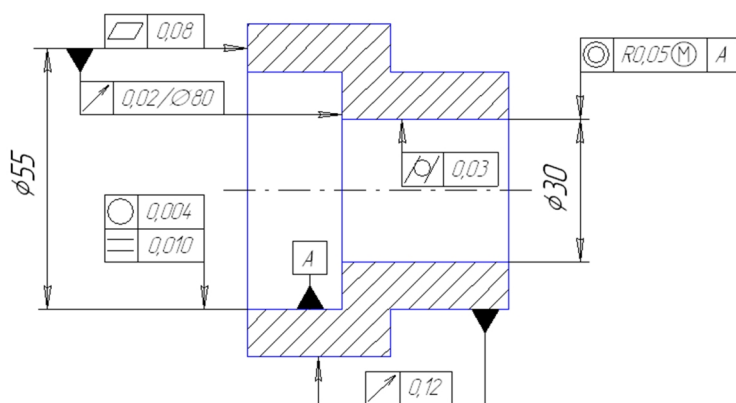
Приклад позначення допусків форми та розташування на кресленнику
